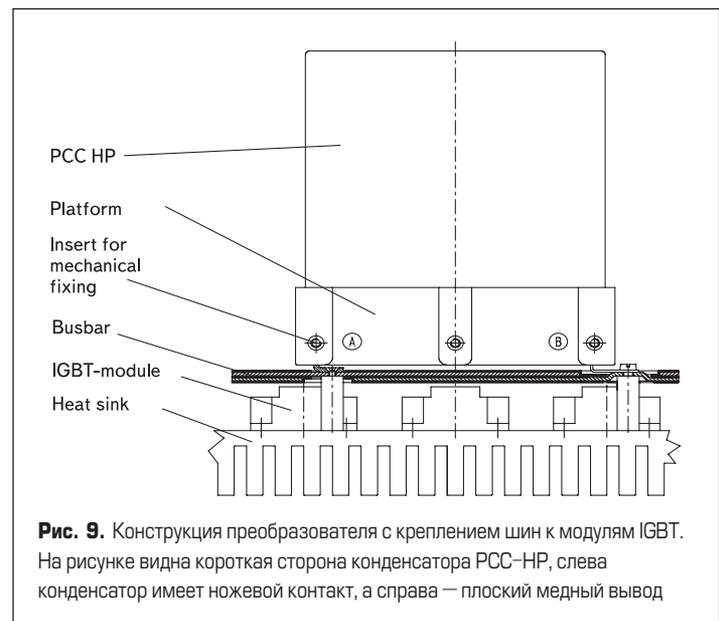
Конструкция преобразователя с креплением шин к модулям IGBT. На рисунке видна короткая сторона конденсатора PCC-HP, слева конденсатор имеет ножевой контакт, а справа — плоский медный вывод
